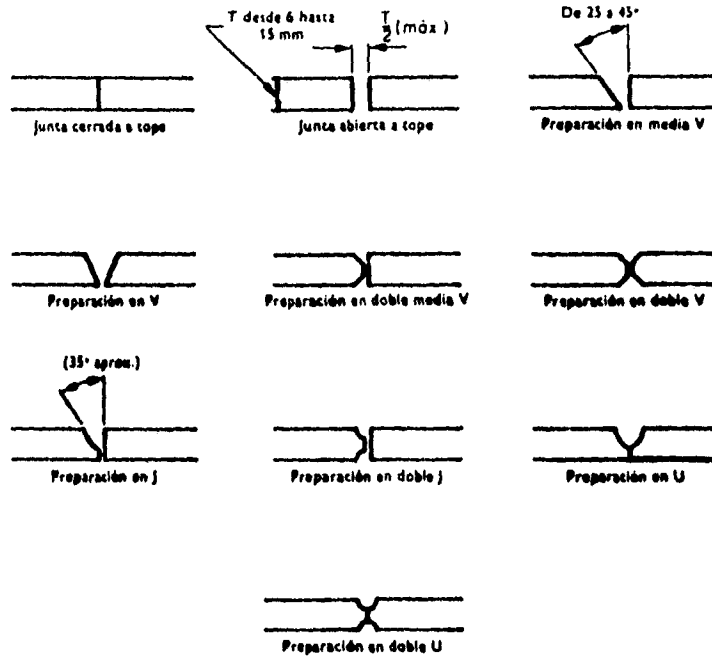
PREPARACION DE LOS BORDES PARA SOLDADURAS A TOPE
